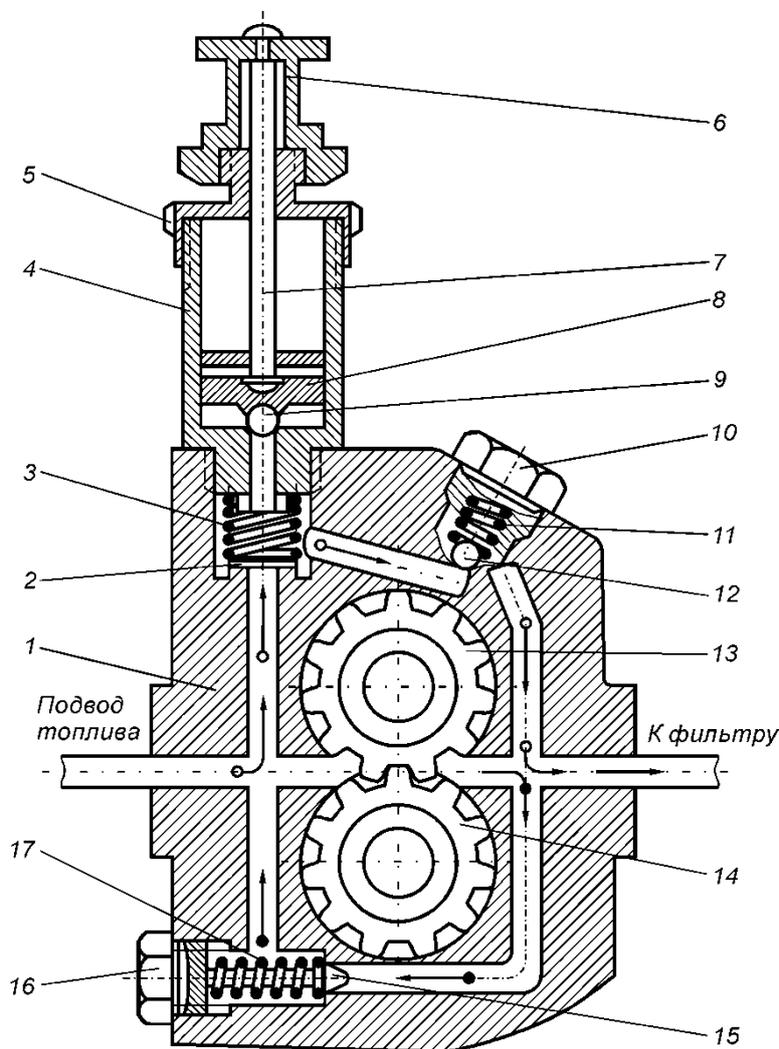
Схема шестеренчатого подкачивающего насоса:
